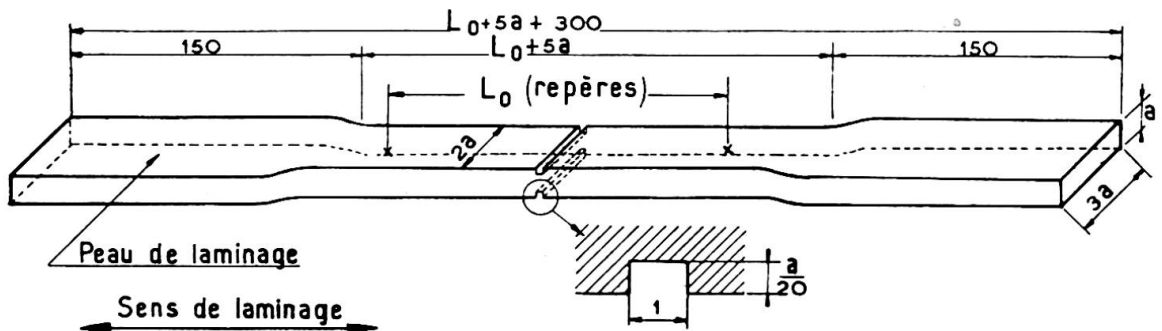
Forme et dimensions de l'éprouvette de l'essai de traction avec entaille préalable.
